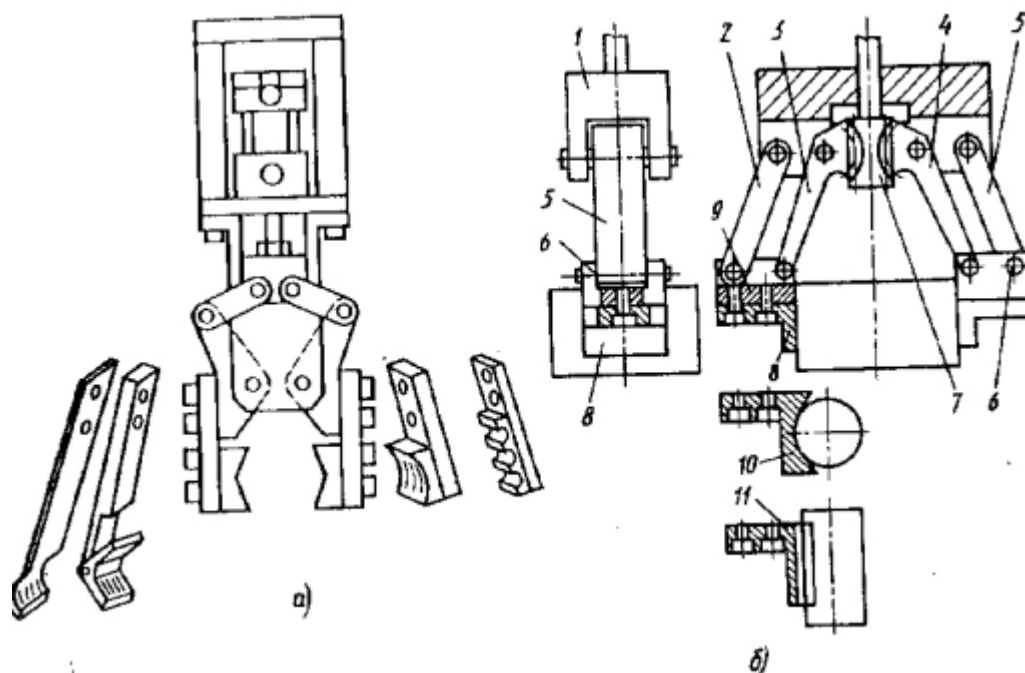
Захватные устройства со сменными губками: а – с шарнирно-рычажным механизмом; б – с зубчатым и рычажными механизмами.
